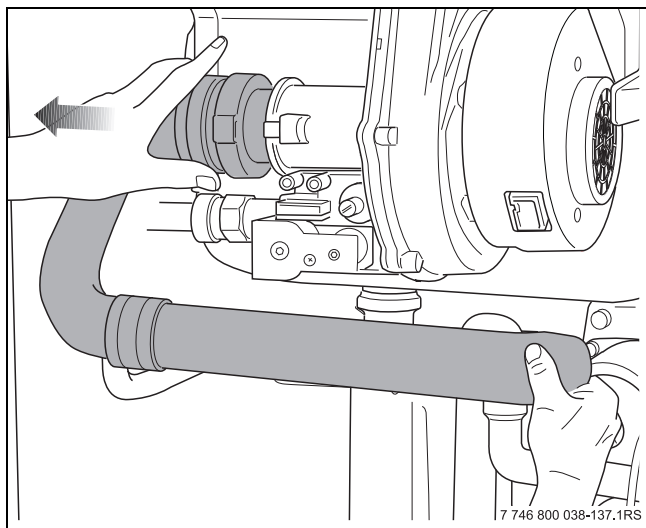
Retirar o tubo de aspiração de ar do ventilador
